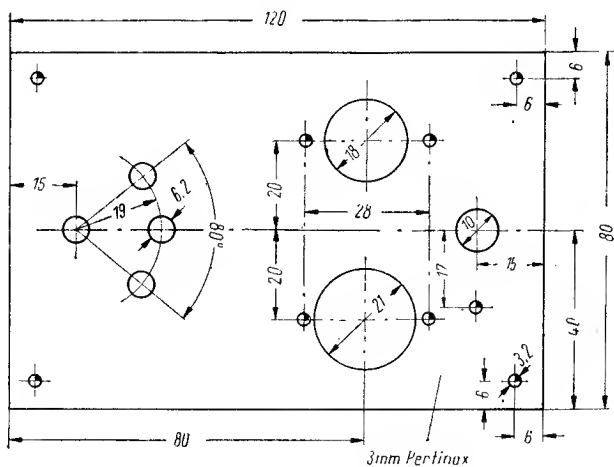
Maßskizze für die Frontplatte des Durchgangsprüfers
